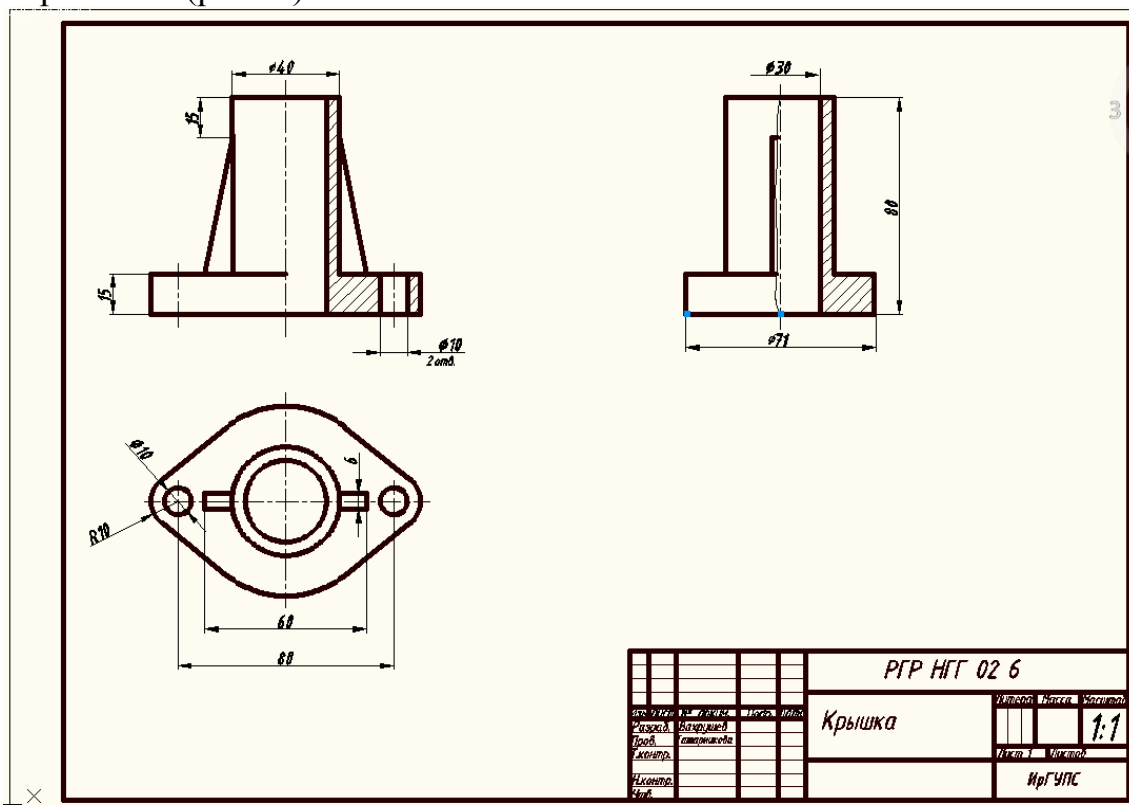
Рабочий чертёж детали «Крышка» - (2D)
